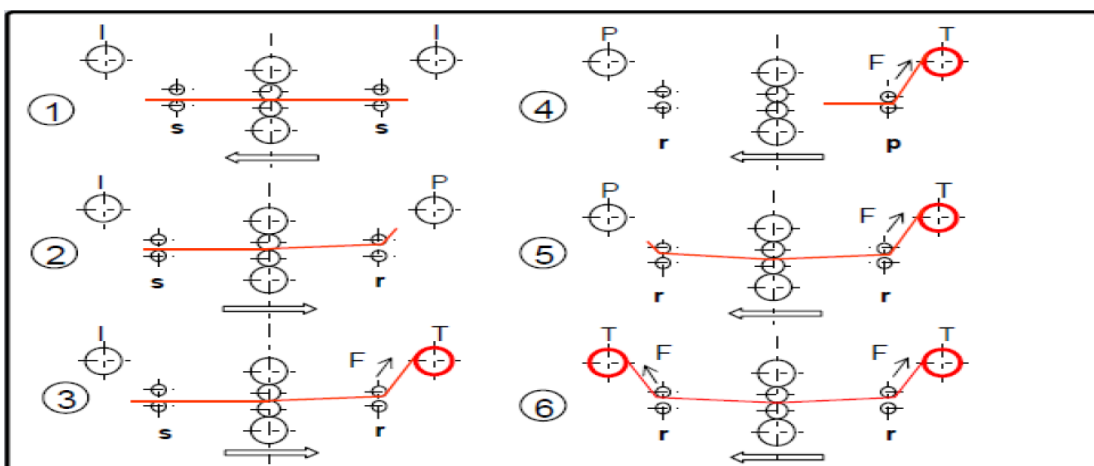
Desenho esquemático de um laminador de tiras a quente - Processo
